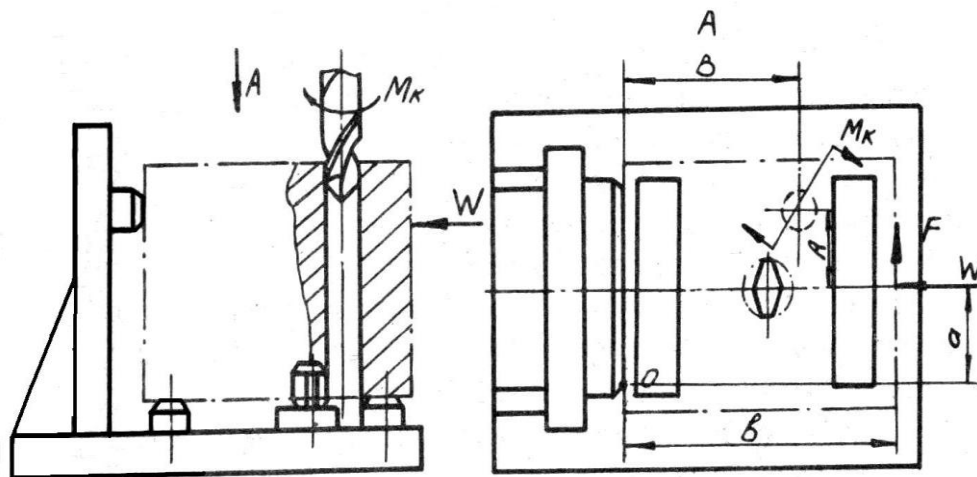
Схема розрахунку затискних зусиль при обробці заготовки на свердильному верстаті установленій нижчою плоскістю на дві опорні пластини і отвором на зрізаний палець, боковою плоскістю на додаткову установочну пластину
